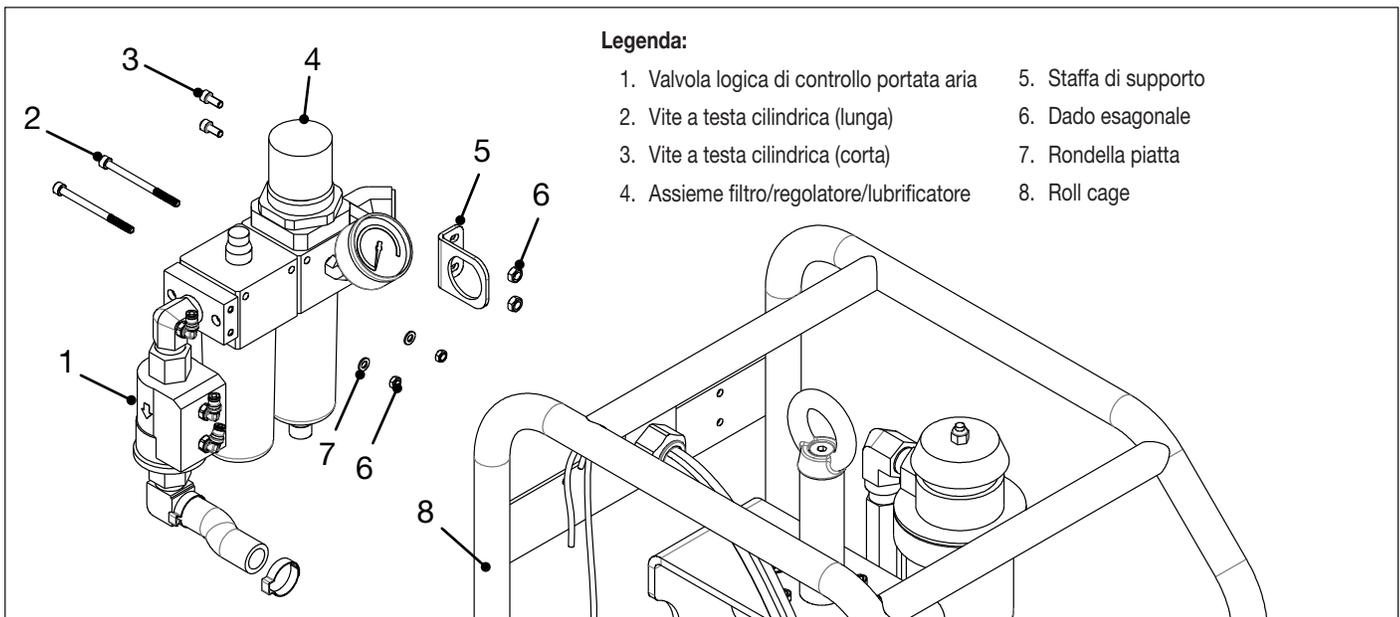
Filtro/regolatore/lubrificatore, valvola di controllo dell'aria e ferramenta di montaggio.
